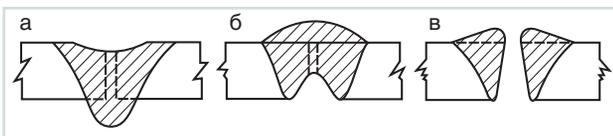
Форма стыкового шва при односторонней сварке на флюсовой подушке: а — при слабом поджатии флюса; б — при сильном поджатии флюса; в — при большом зазоре в стыке
